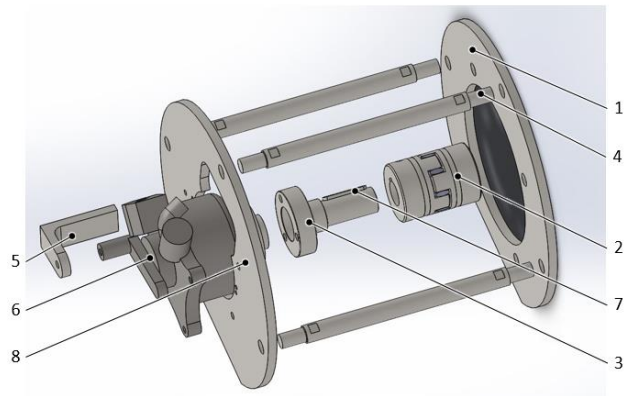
Explosionsdarstellung der einzelnen Bauteile im CAD.
